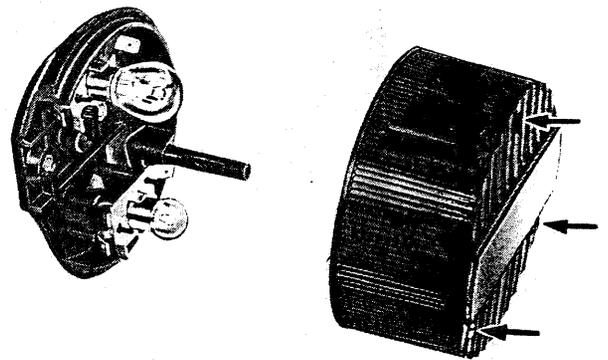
Feu stop-arrière-plaque (partiellement ouvert en coupant)
